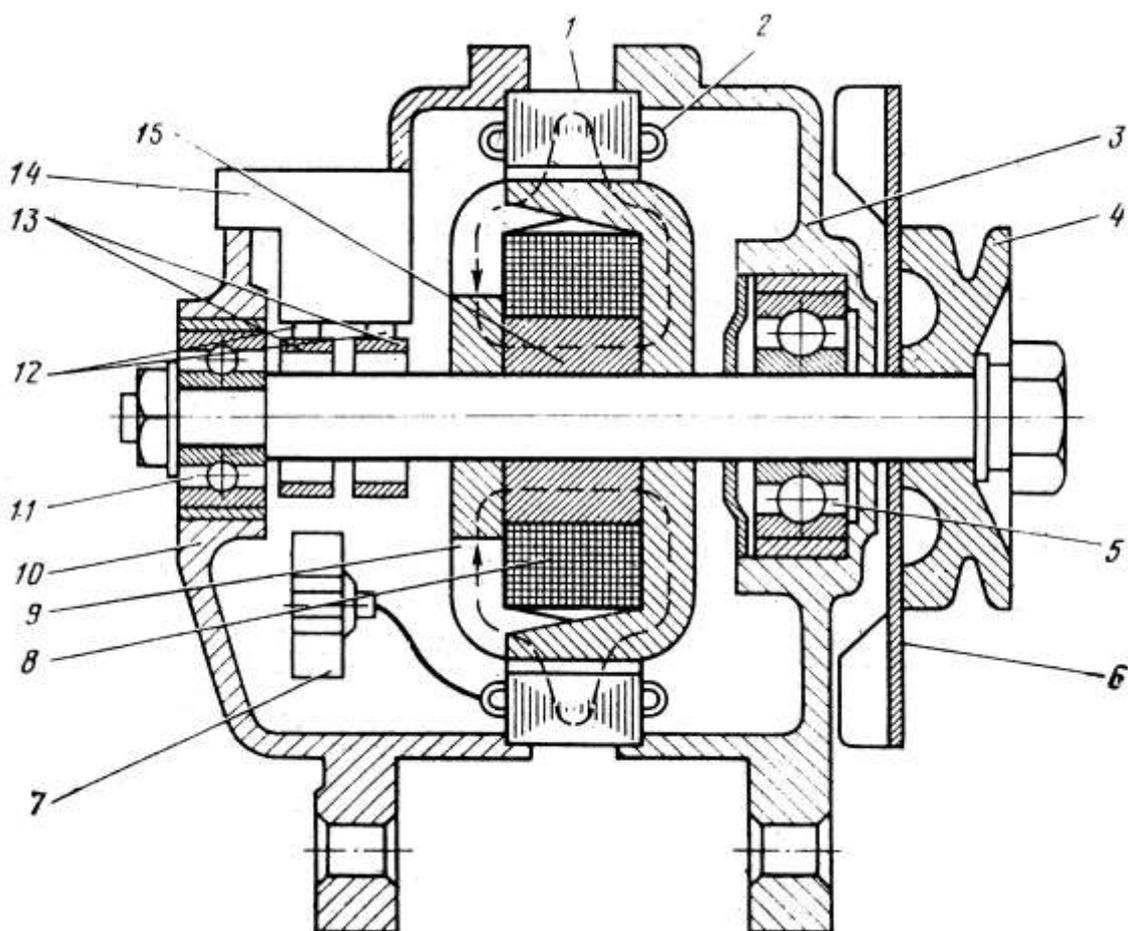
Генератор переменного тока с клювообразным ротором: 1 – статор; 2 – обмотка статора; 3, 10 – крышка; 4 – шкив; 5, 11 – шарикоподшипники; 6 – крыльчатка; 7 – выпрямительный блок; 8 – обмотка возбуждения; 9 – клювообразный полюс ротора; 12 – щетка; 13 – контактные кольца; 14 – щеткодержатель; 15 – втулка
